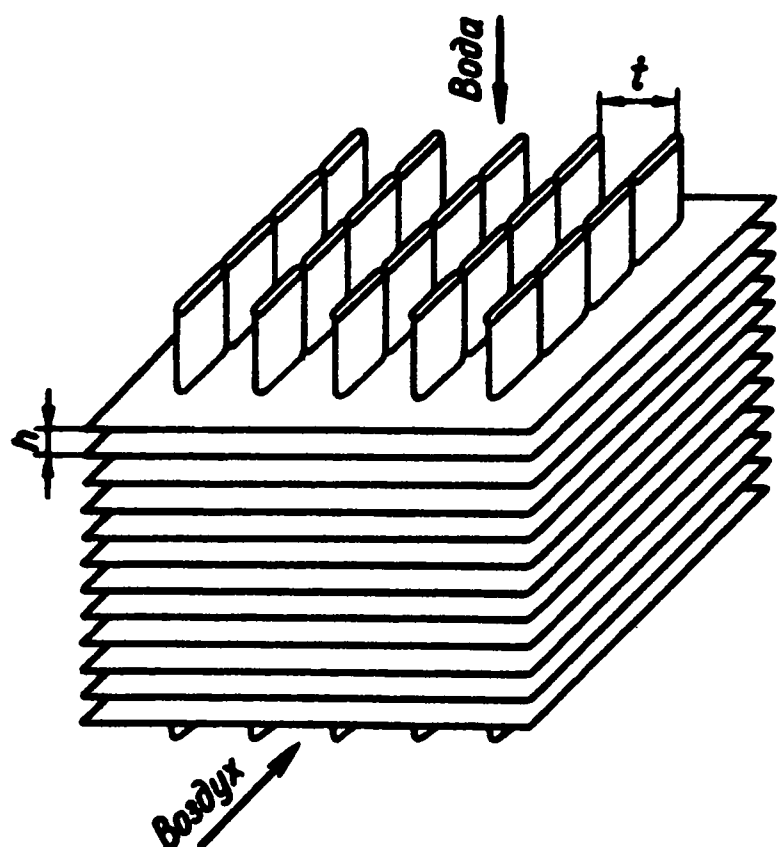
Серийный тип конструкции водяного радиатора для тракторов и комбайнов
